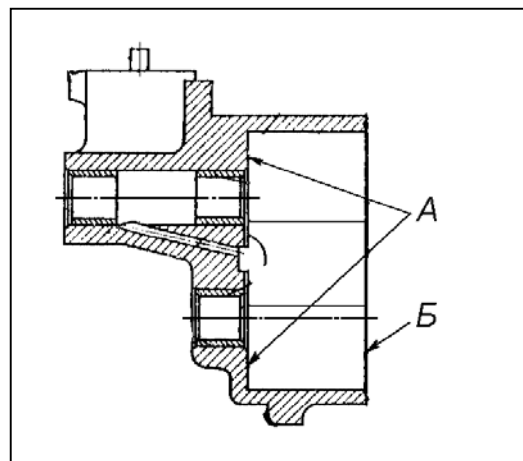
К контролю и восстановлению глубины гнезд корпуса.
